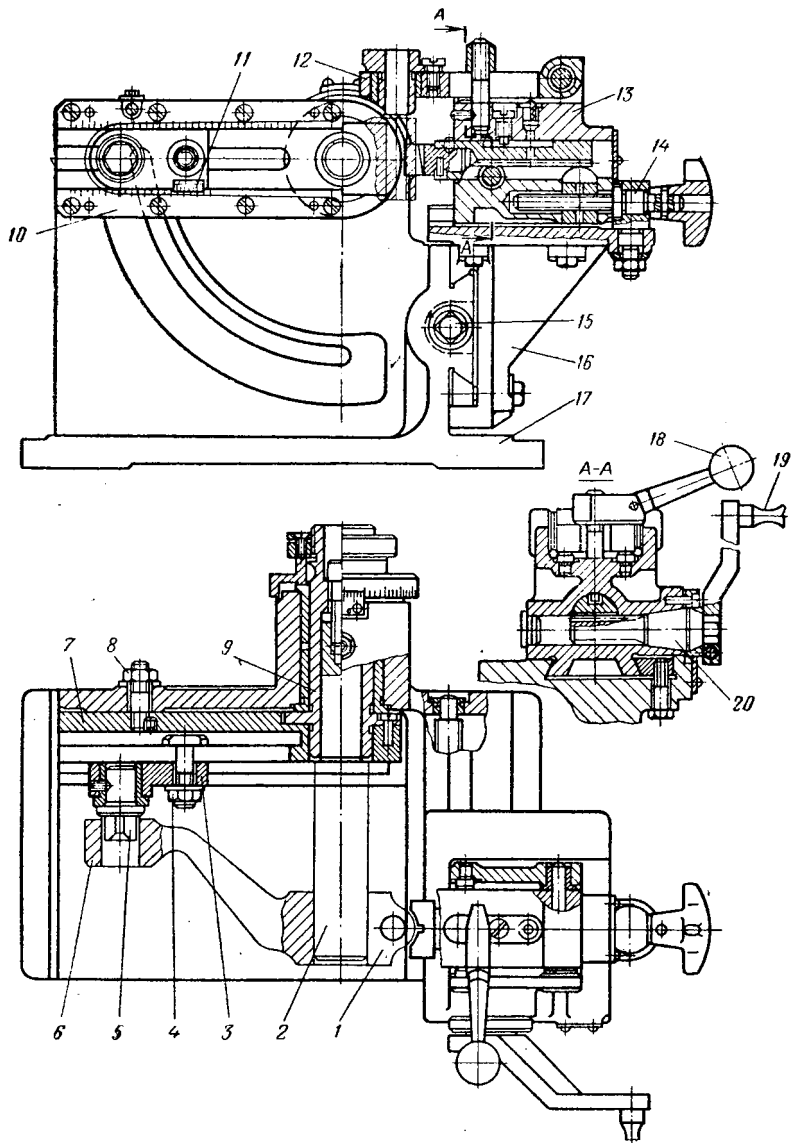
Универсально-наладочное приспособление для сверления отверстий и нарезания резьбы в рычагах под зажим
